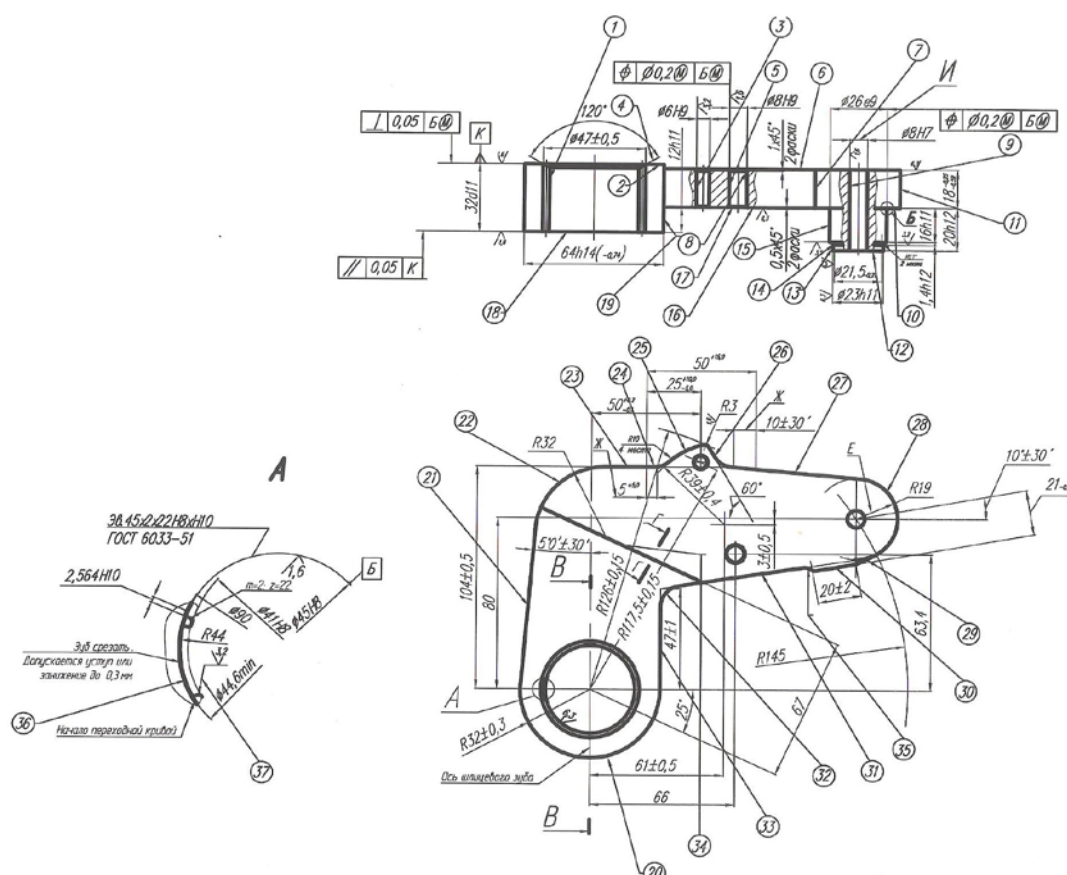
Нумерация обрабатываемых поверхностей детали
